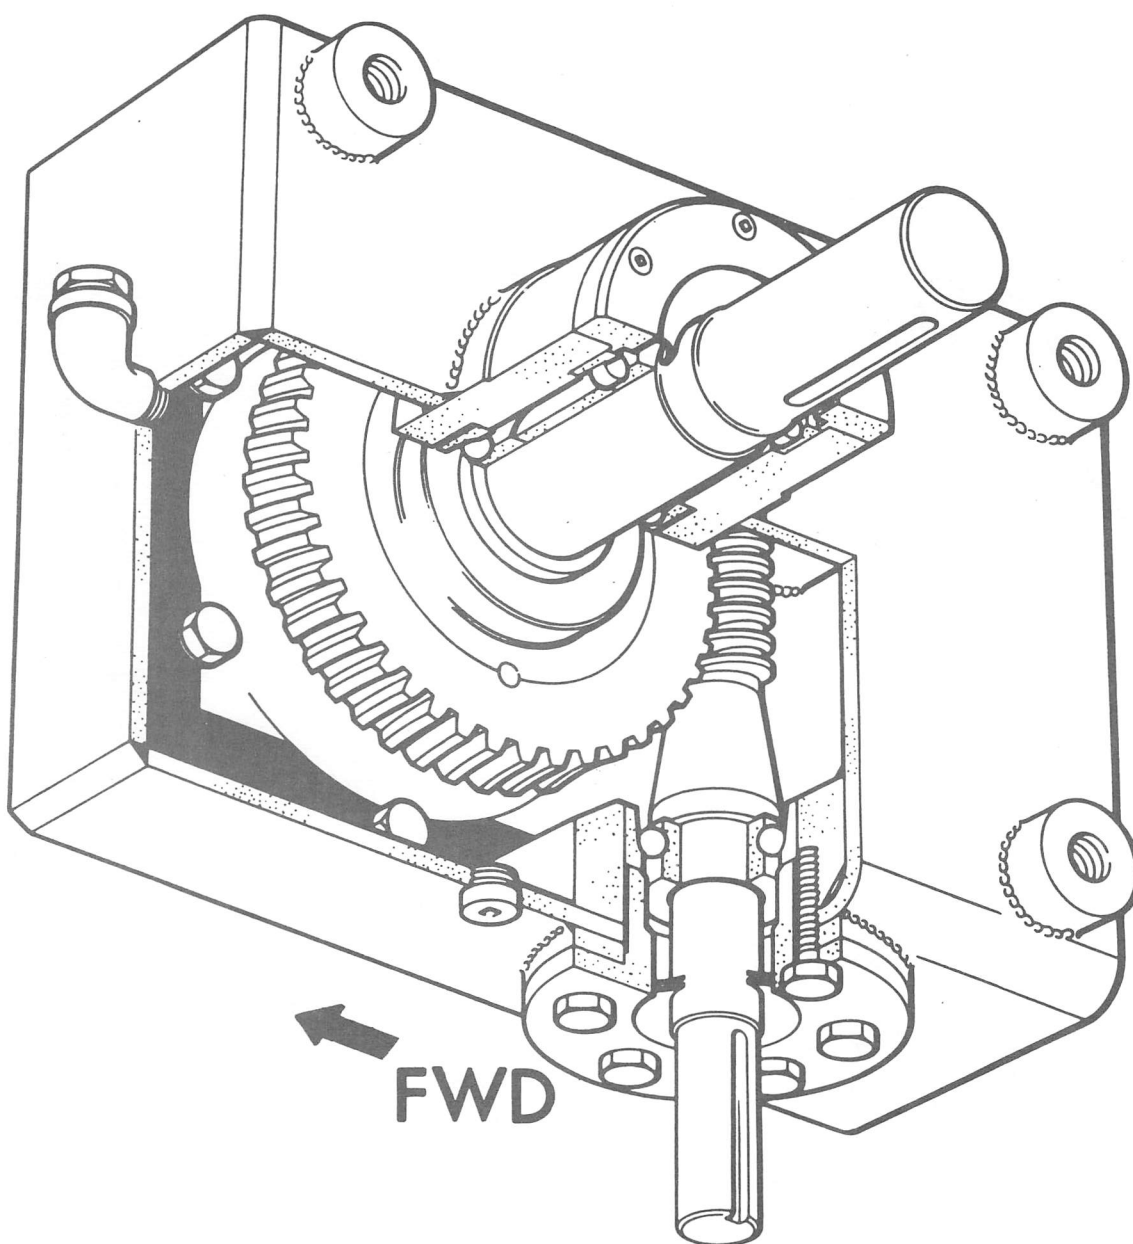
Engrenage démultiplicateur à vis sans fin
